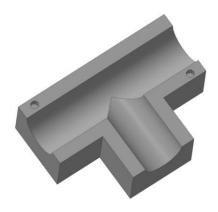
Половина стержневого ящика для изготовления стержня
